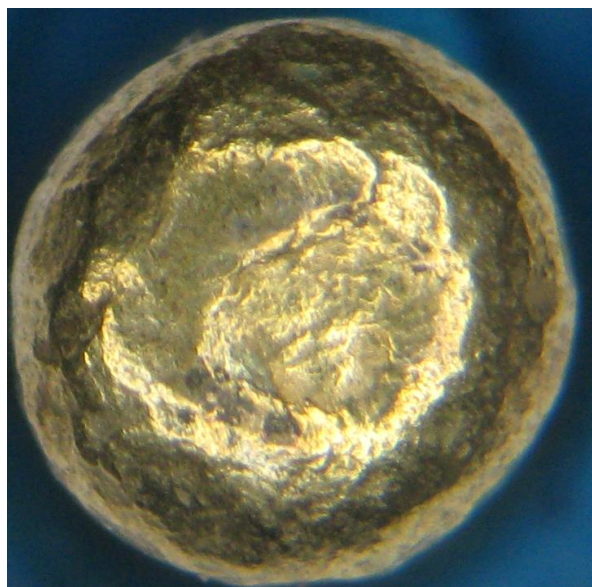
След на вершине одного из штифтов корпуса в месте его контакта со штифтом цилиндра
